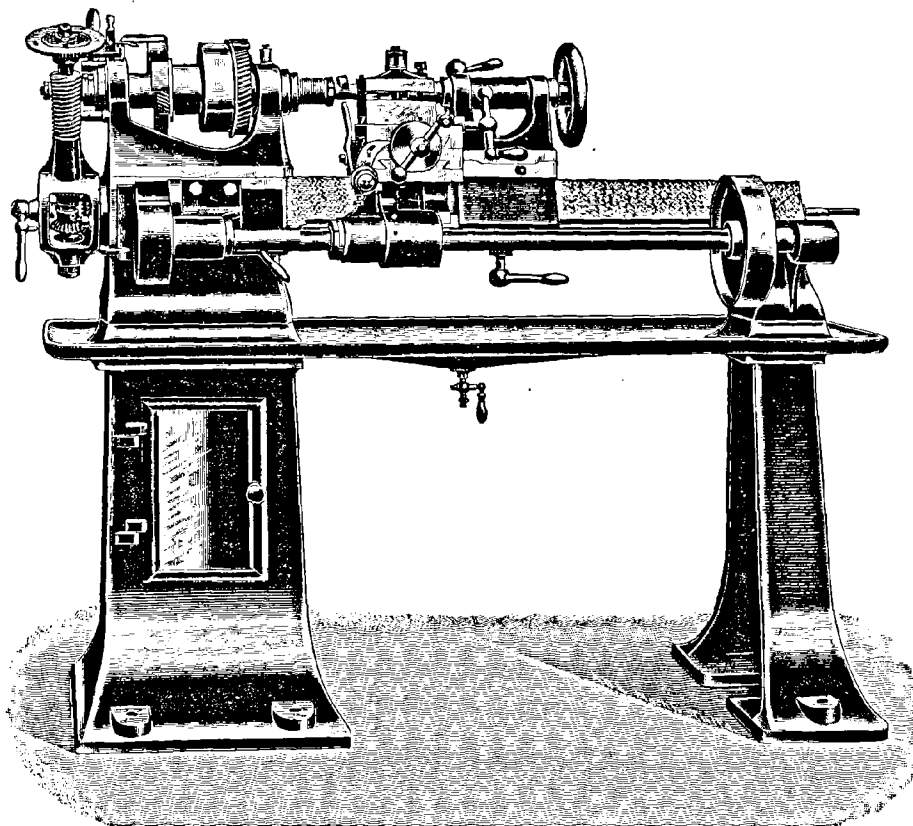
Machine automatique pour la fabrication des fraises à dépointe.
